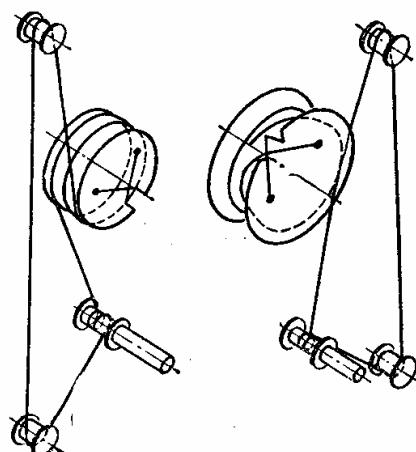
Кинематическая схема верньерного устройства радиоприемника «Ленинград-002»
